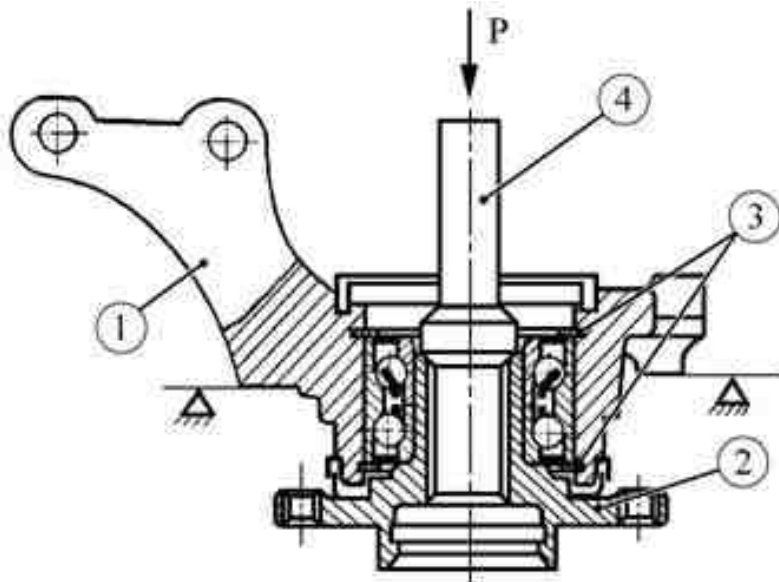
Выпрессовка ступицы переднего колеса из поворотного кулака:
